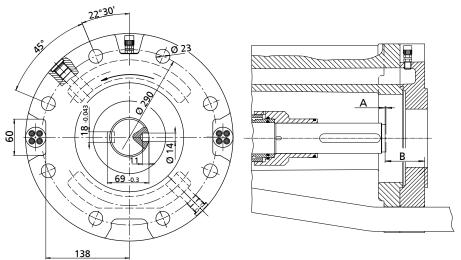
Dimensión de acoplamiento 14D, dimensiones [mm]
